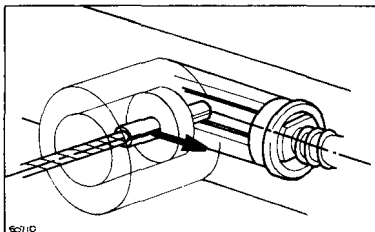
30 Извлечение стопорного штифта тормозного цилиндра Bendix
